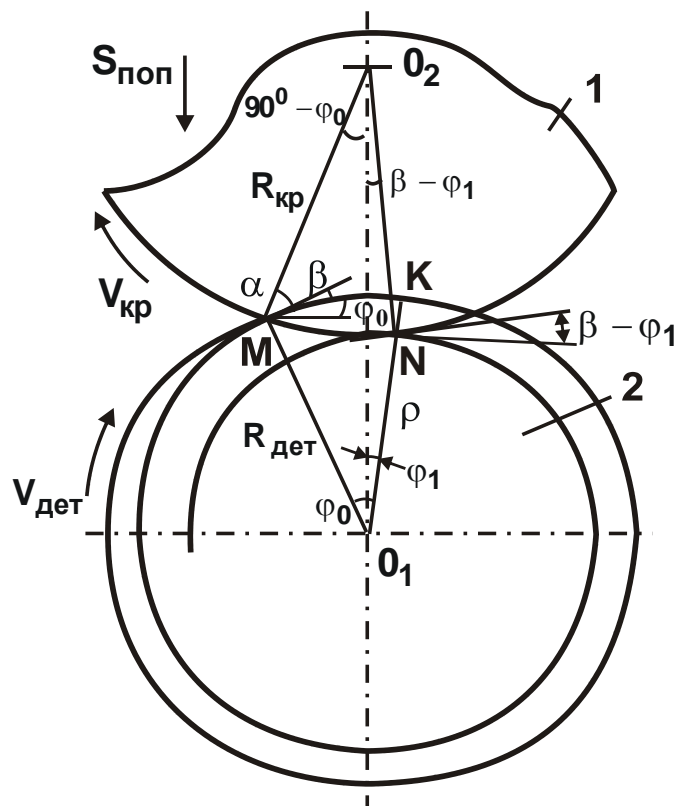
Розрахункова схема параметрів круглого урізного шліфування: 1 – круг; 2 – оброблювана деталь
